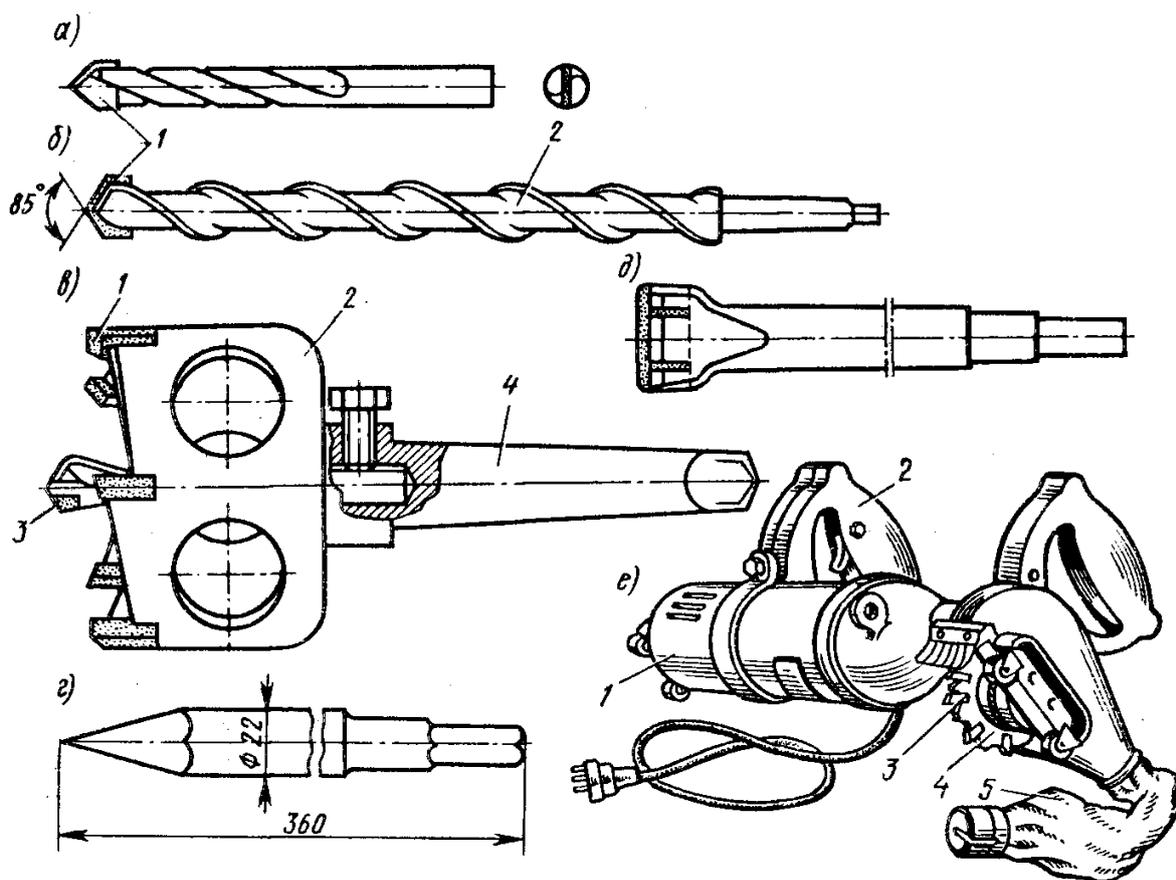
Инструмент для пробивки отверстий, ниш и борозд: а - спиральное сверло; б - сверло из витой стали для глубоких отверстий: 1 - пластинки твердого сплава; 2 - корпус; 3 - центрирующее сверло; 4 - хвостовик; в - коронка; г - лом к пневматическому молотку для пробивки ниш и борозд; д - скарпель; е - механизм для пробивки борозд: 1 - электропривод; 2 - рукоятка; 3 - пластинка твердого сплава; 4 - фреза; 5 - пылесборник
